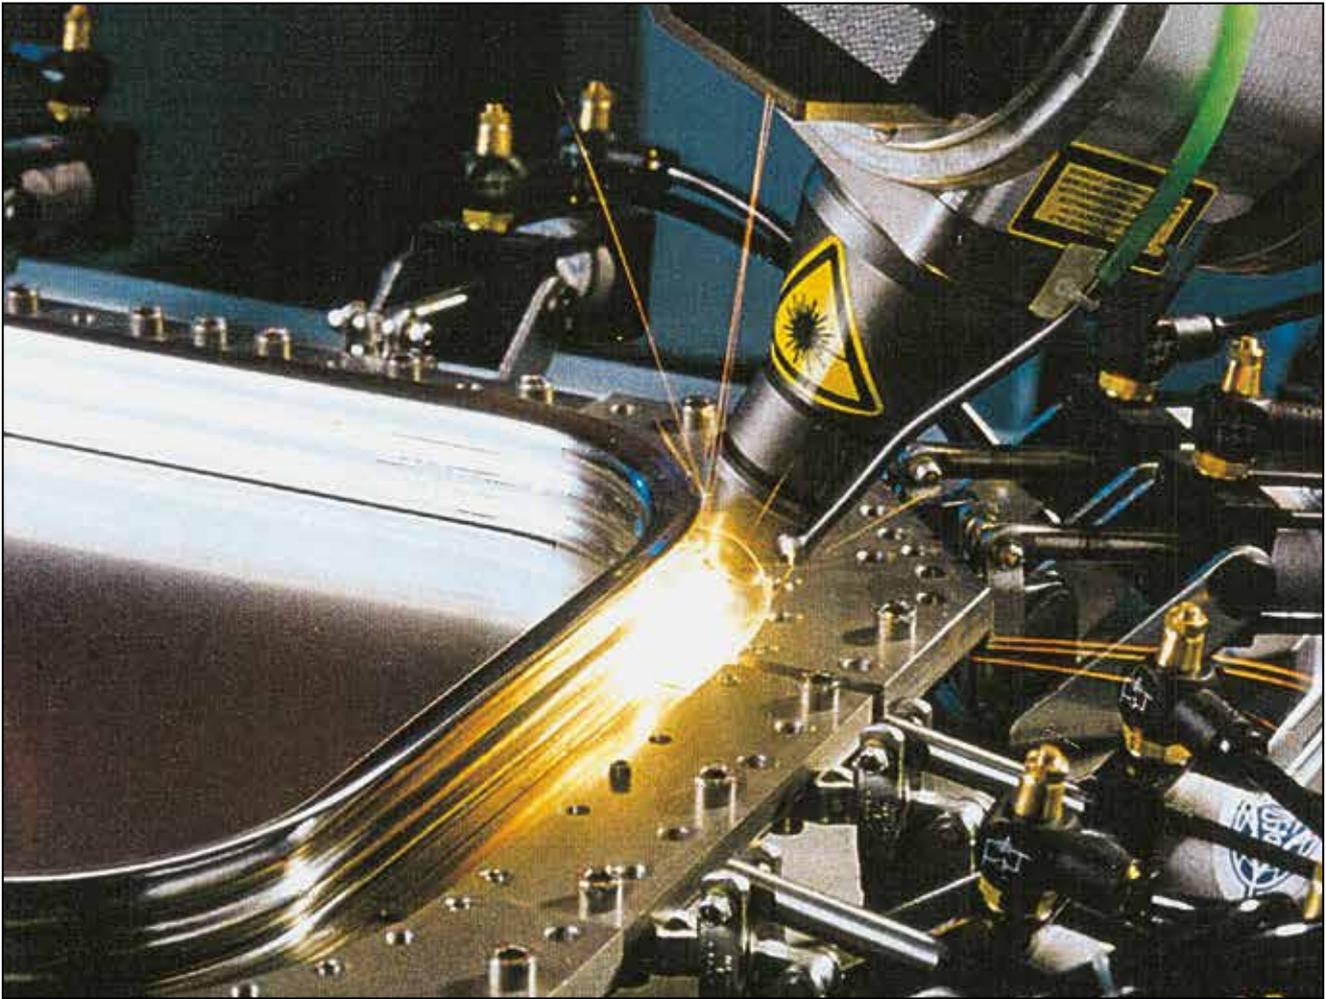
Schweißen von Membranringen mit einem Nd:YAG-Laser
